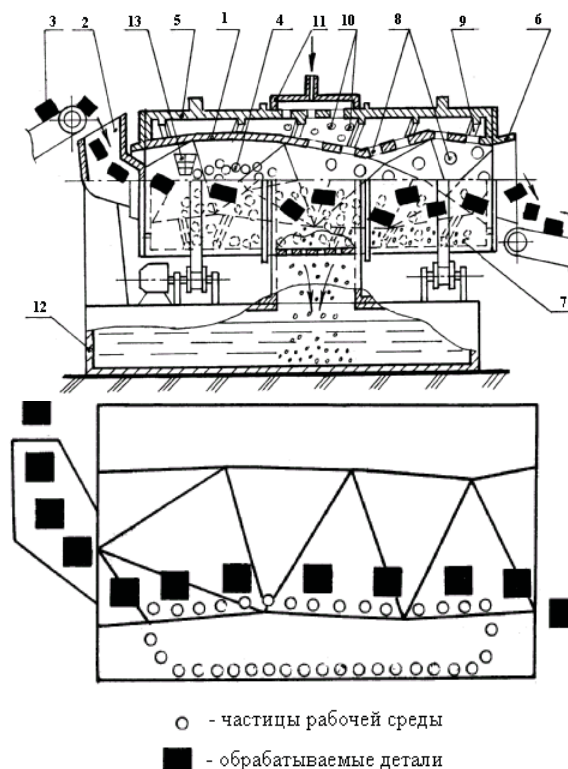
Установка и схема движения деталей и частиц рабочих сред в установке для непрерывной УОЗО деталей
